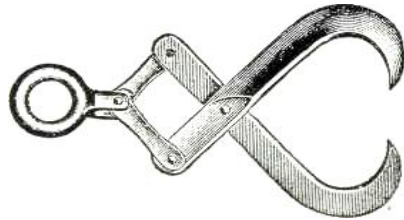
Подвійний шарнірний гачок Крея-Шоттлера
